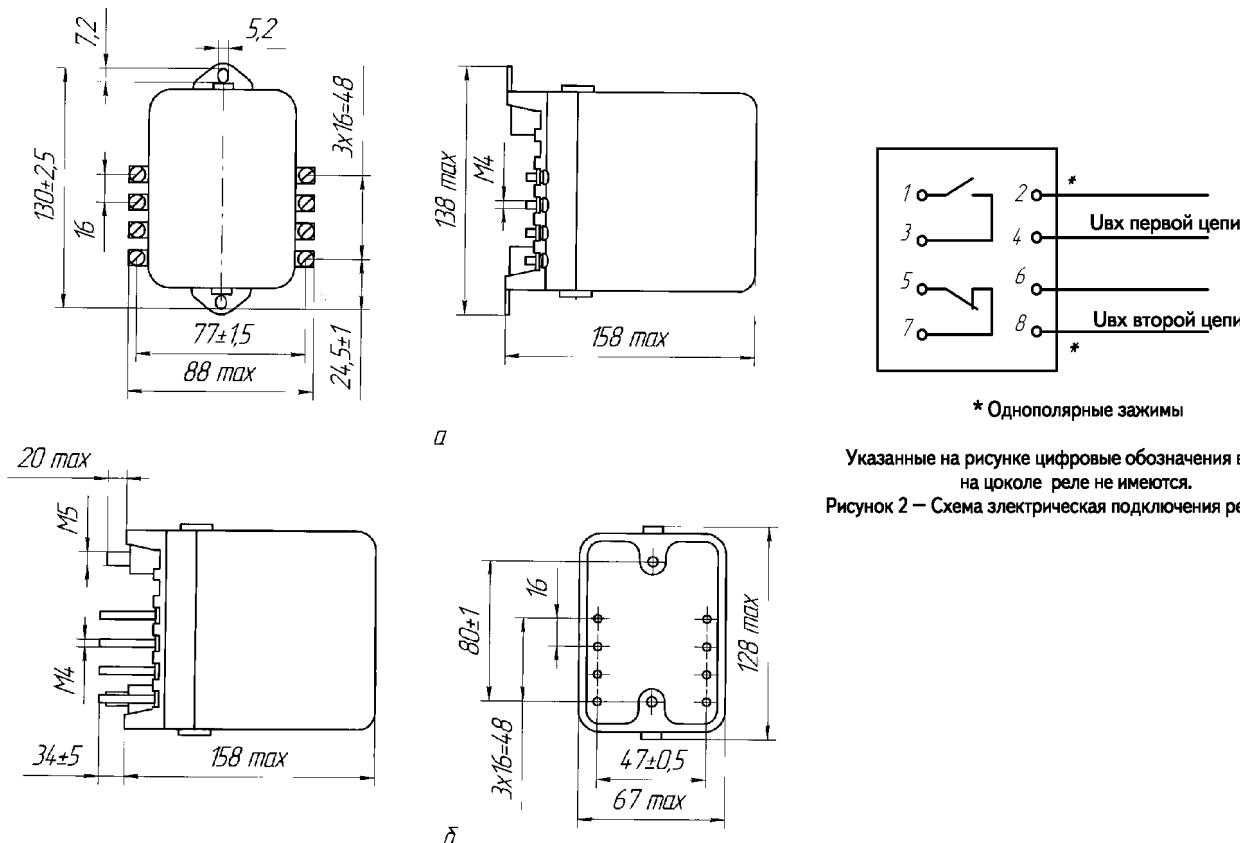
Габаритные, установочные и присоединительные размеры реле типа РН 55.
